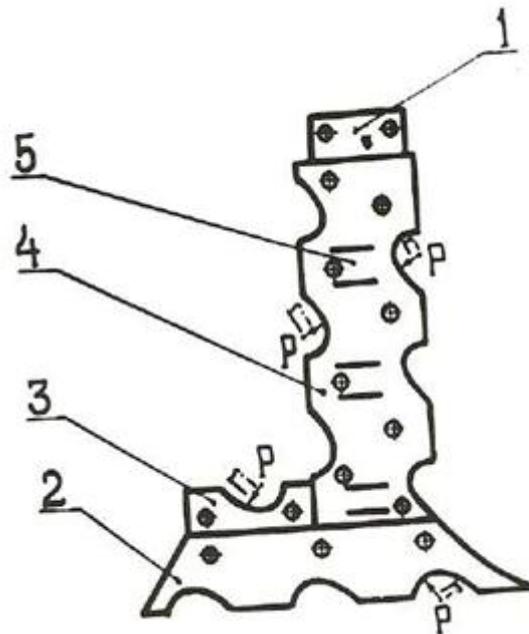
Зубчатий безвідвальний корпус плуга
